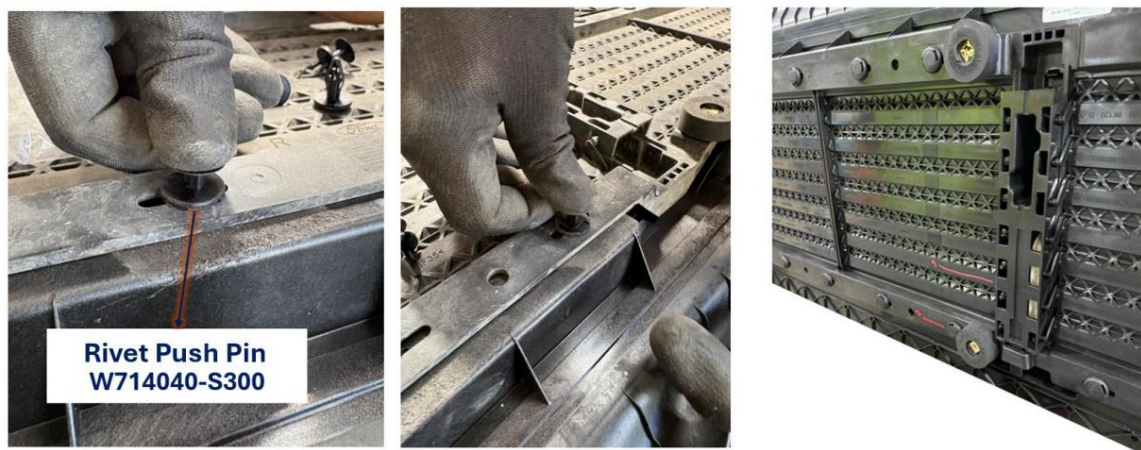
Assemblage par rivet et goupille de poussée du conduit supérieur et du déflecteur d'air
